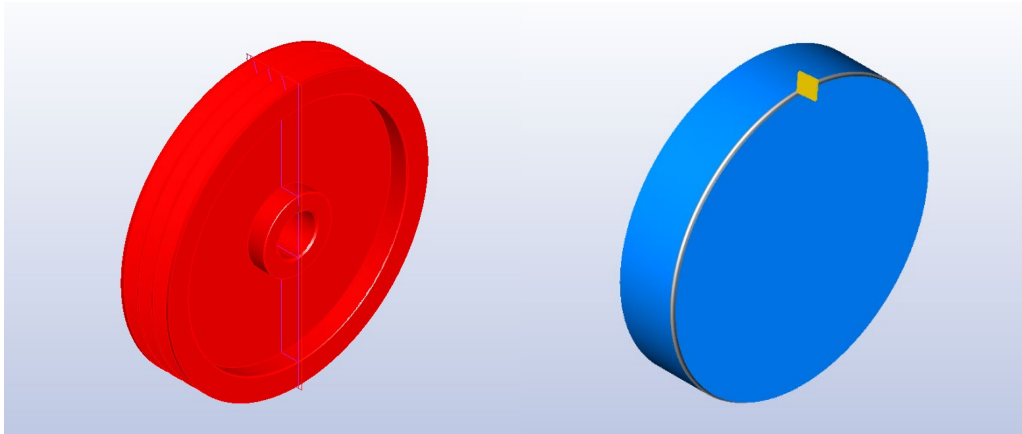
Тривимірна модель заготовки та обробленого шківів.
